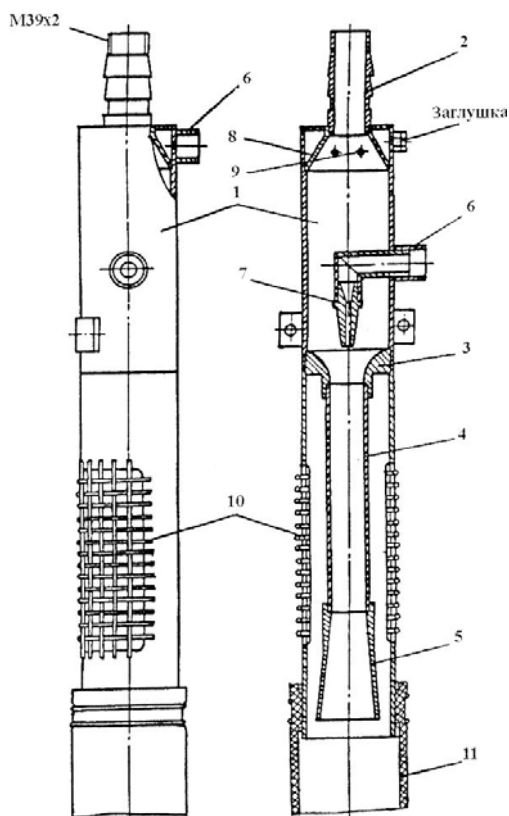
Общий вид универсального аппарата УПА – 1М
